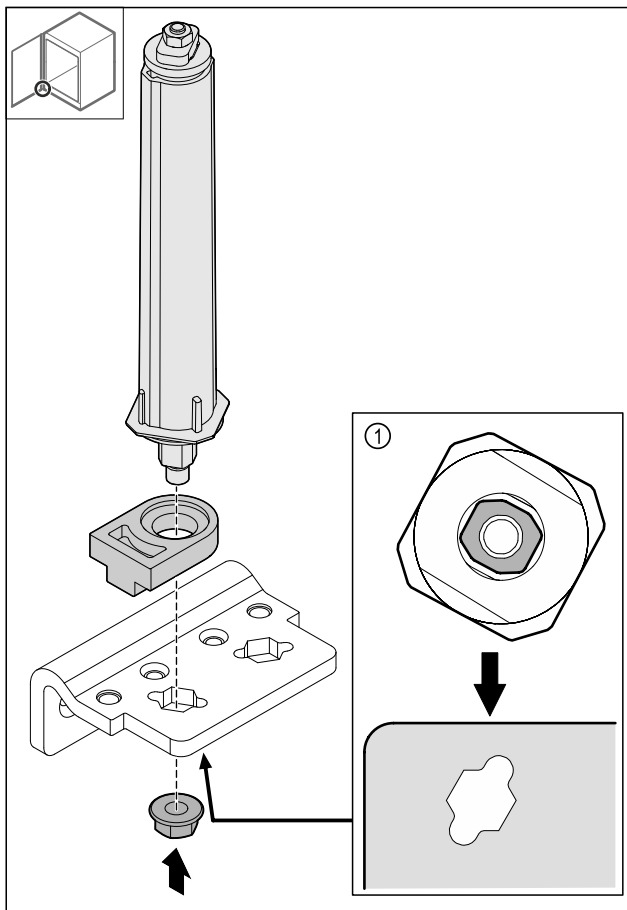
Pogled od spodaj; Fig. 39 (1)
